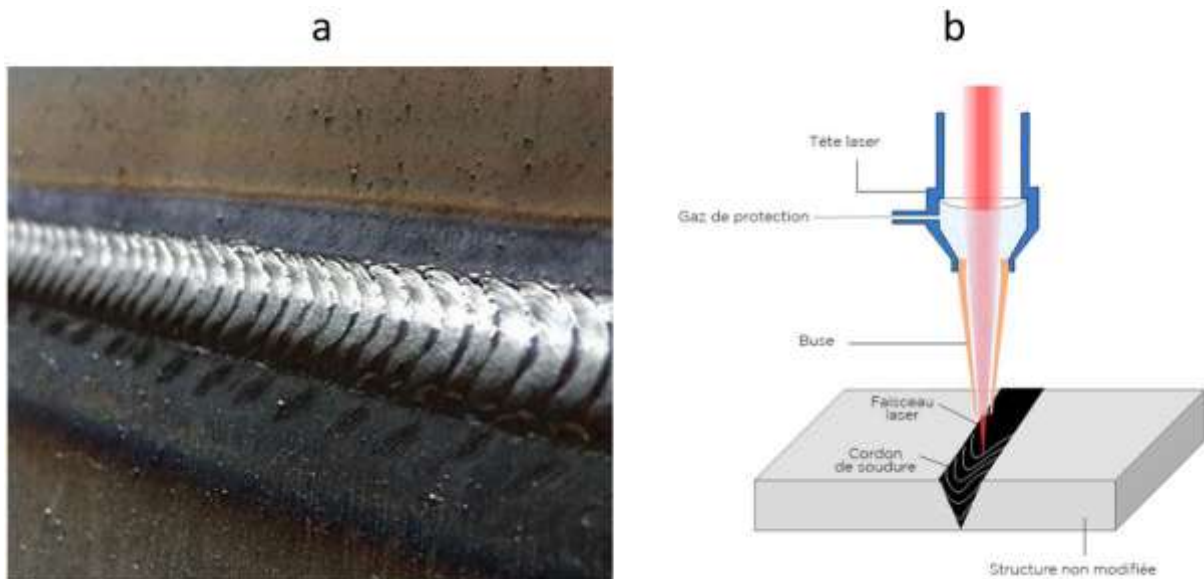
(a) exemple d'un cordon obtenu par soudage à l'arc. (b) Schéma de principe du soudage laser sans métal d'apport.
